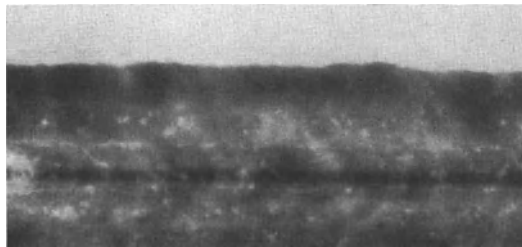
Röntgenbild einer V-Naht-Lichtbogenschweißung mit kleinen Gasblasen (runde weiße Punkte). Hellere und dunklere Zonen sind Querschnittsunterschiede der Schweißraupe.
